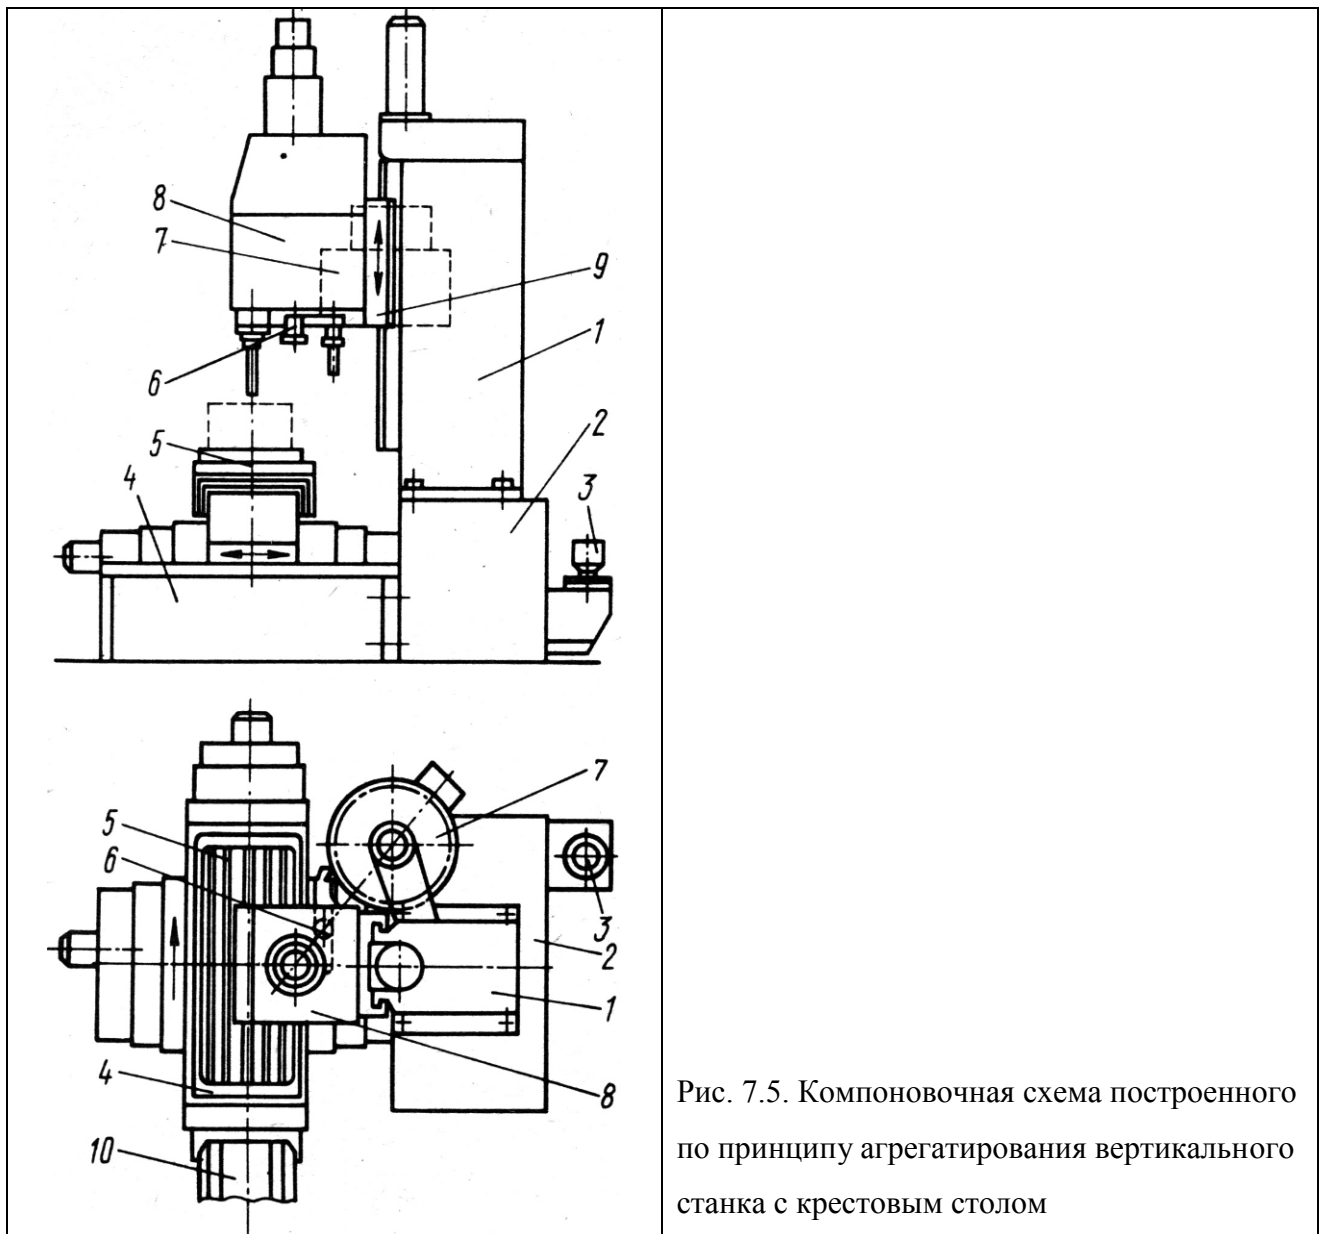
Компонировочная схема построенного по принципу агрегатирования вертикального станка с крестовым столом
